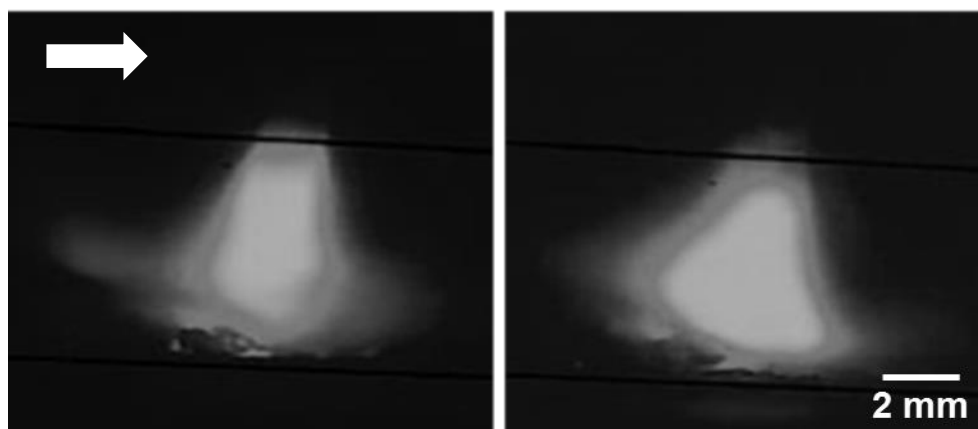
Imagens do arco elétrico da soldagem A-MIG com  $\text{CaCO}_3$  a 190A. A direção de soldagem é indicada pela seta.
